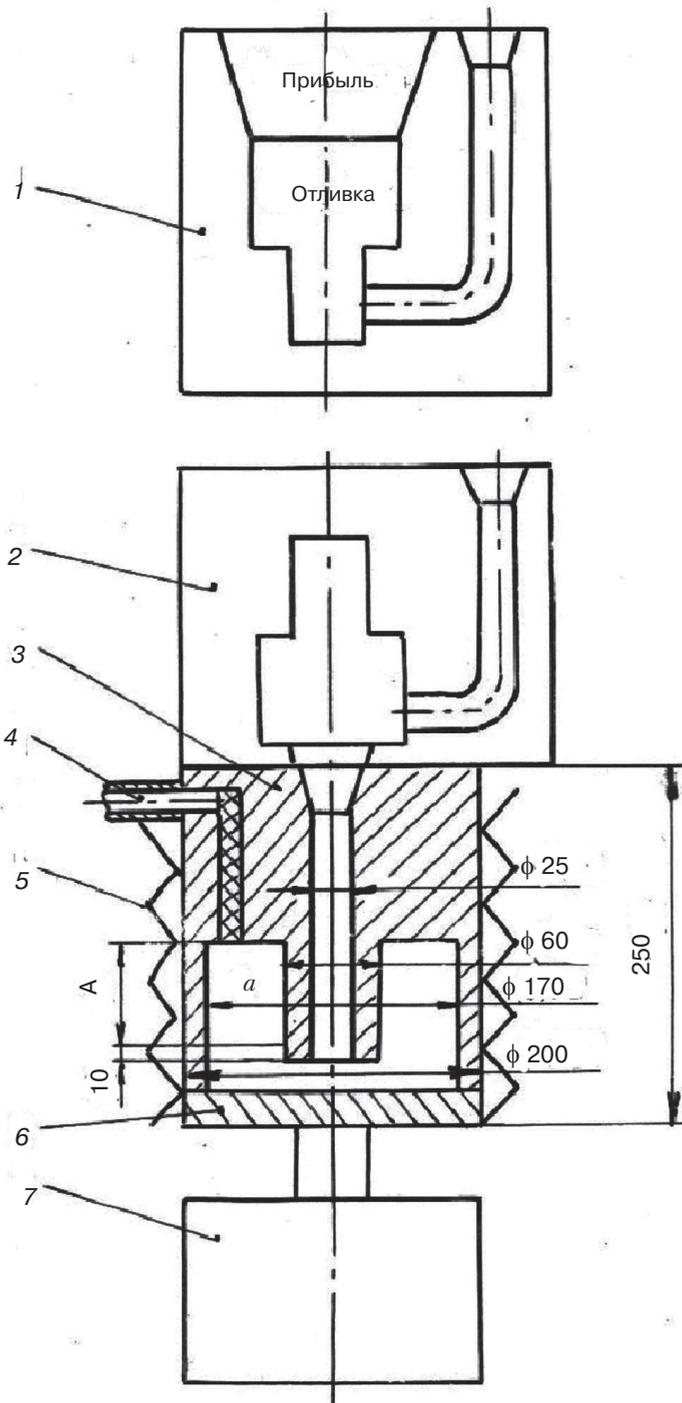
Технологическая схема кокильного литья с автономным питанием затвердевающей отливки под низким газовым давлением: 1 – исходный кокиль; 2 – преобразованный кокиль; 3 – корпус питающего устройства; 4 – воздухопровод, заполненный огнеупорной ватой; 5 – обогревательная печь; 6 – днище питающего устройства; 7 – пневмоцилиндр
